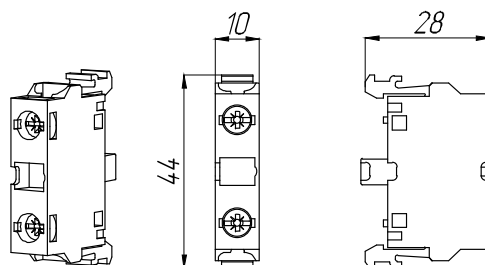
Общий вид и габаритные размеры контактного блока MCB-10 для кнопки пуск SB1
